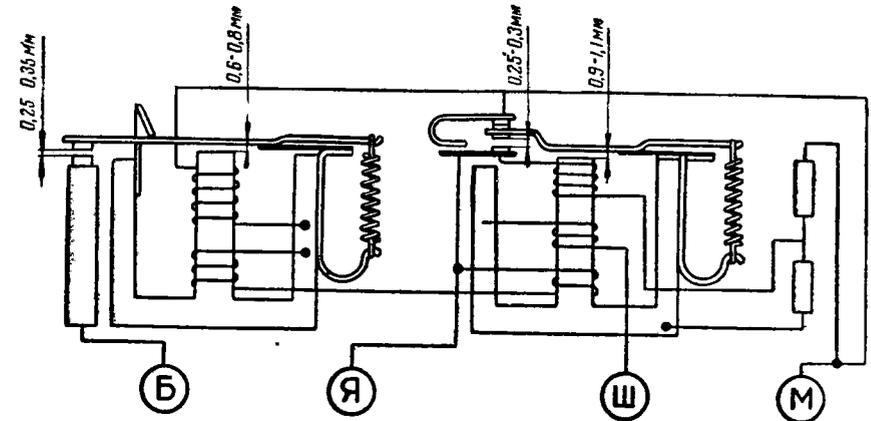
Схема регулировки зазоров реле-регулятора ИЖ.
